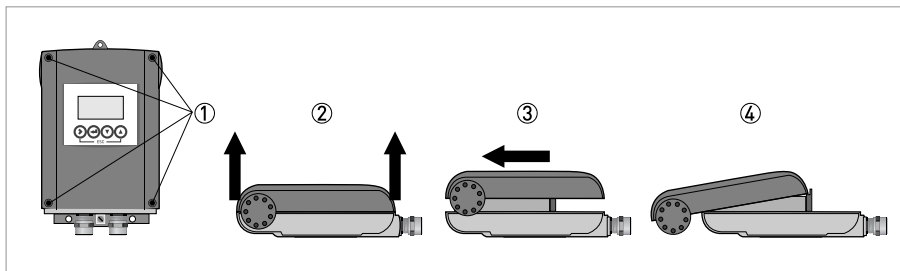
Öffnen und Schließen des Aluminiumgehäuses
